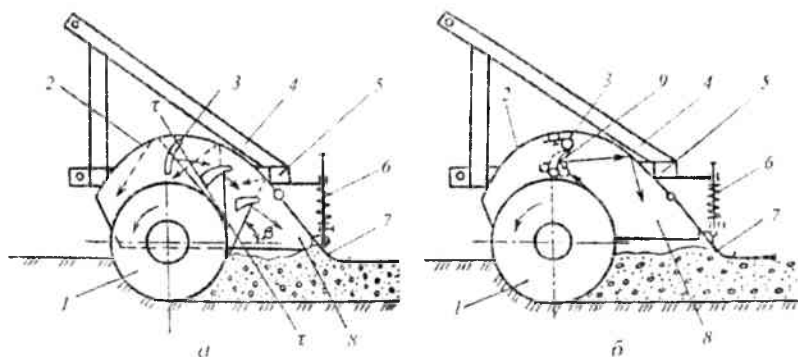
Кожухи и фартуки-выравниватели с жесткими (а) и упругими (б) рефлекторами: 1 – ротор; 2 – кожух; 3 – ось; 4 – навесное устройство; 5 – рама; 6 – пружинно-поводковый нагрузчик; 7 – фартук-выравниватель; 8 – боковина; 9 – рефлектор
